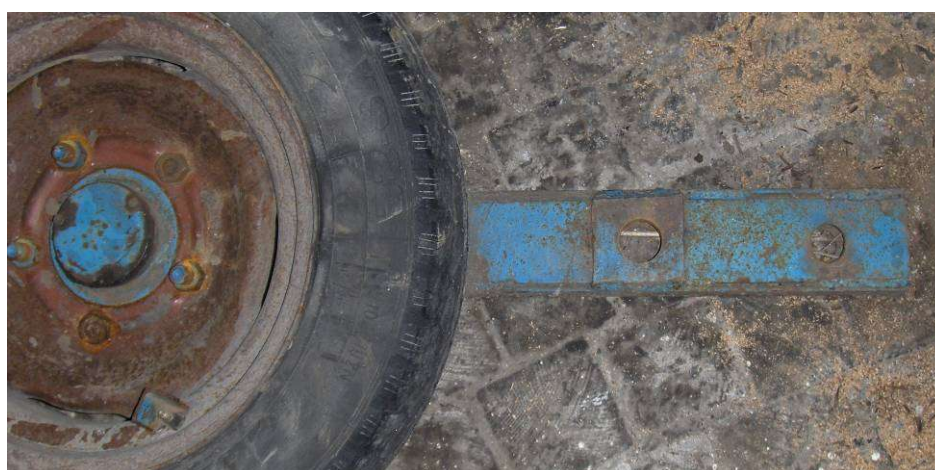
Зноси деталей ходової частини культиватора КПС-4.
